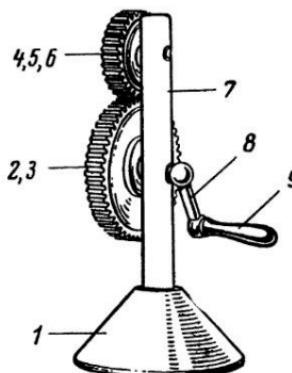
Модель цилиндрической зубчатой передачи: 1 — основание; 2 — вал привода; 3 — ведущее колесо; 4 — ось ведомого колеса; 5 — ведомое колесо; 6 — шайба; 7 — стойка; 8 — рычаг привода; 9 — ручка.
